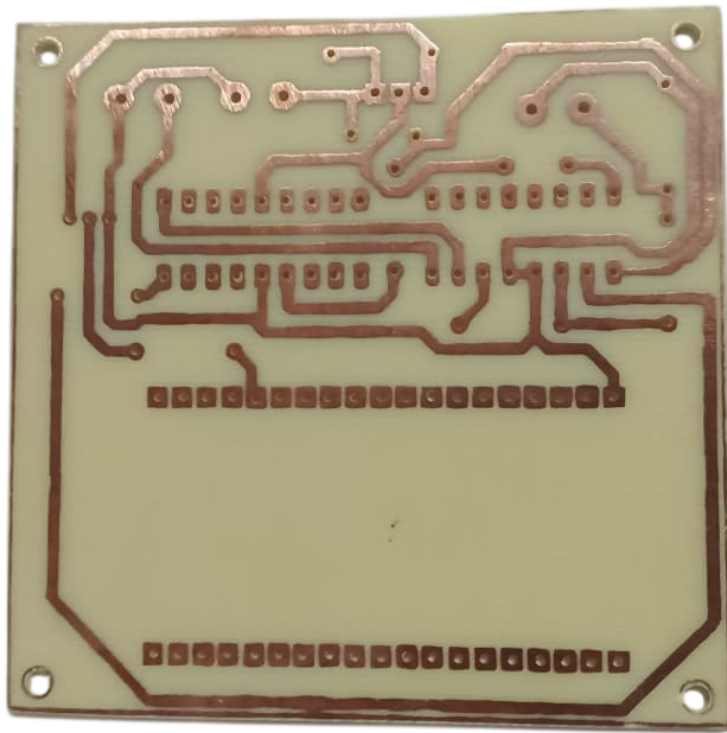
Ruteado de placa PCB de simulador mecánico. Autor Propio
